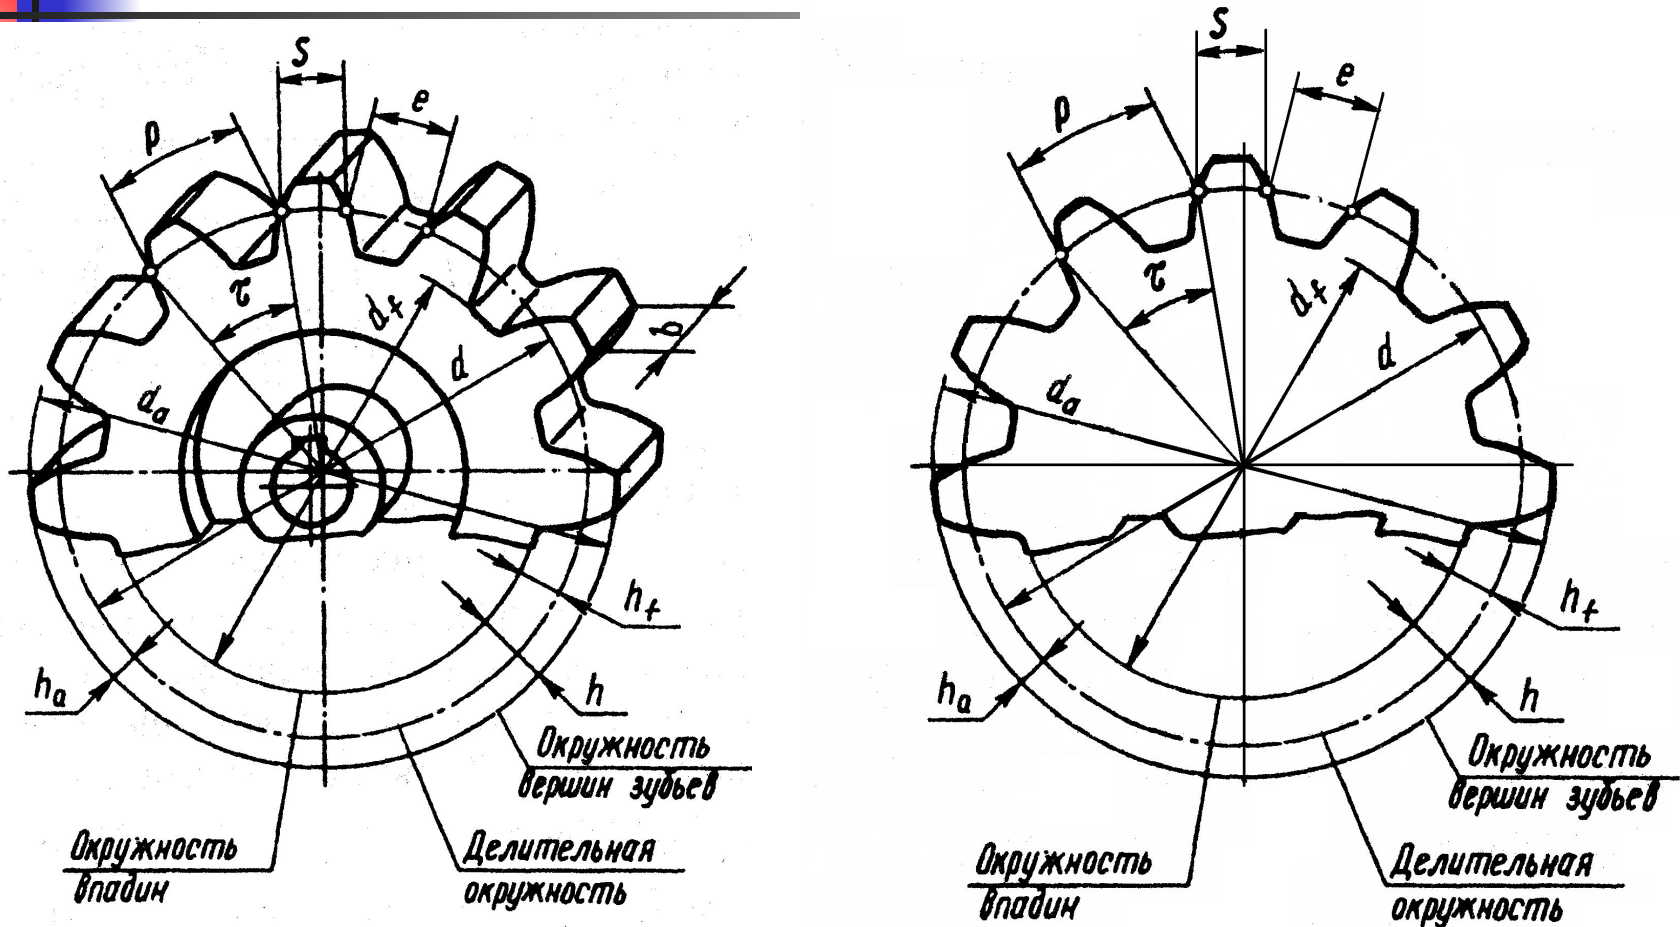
Цилиндрическое колесо с прямыми зубьями
